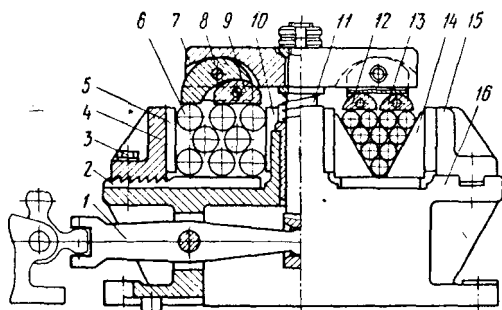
Универсально-наладочное приспособление для фрезерования торцов
